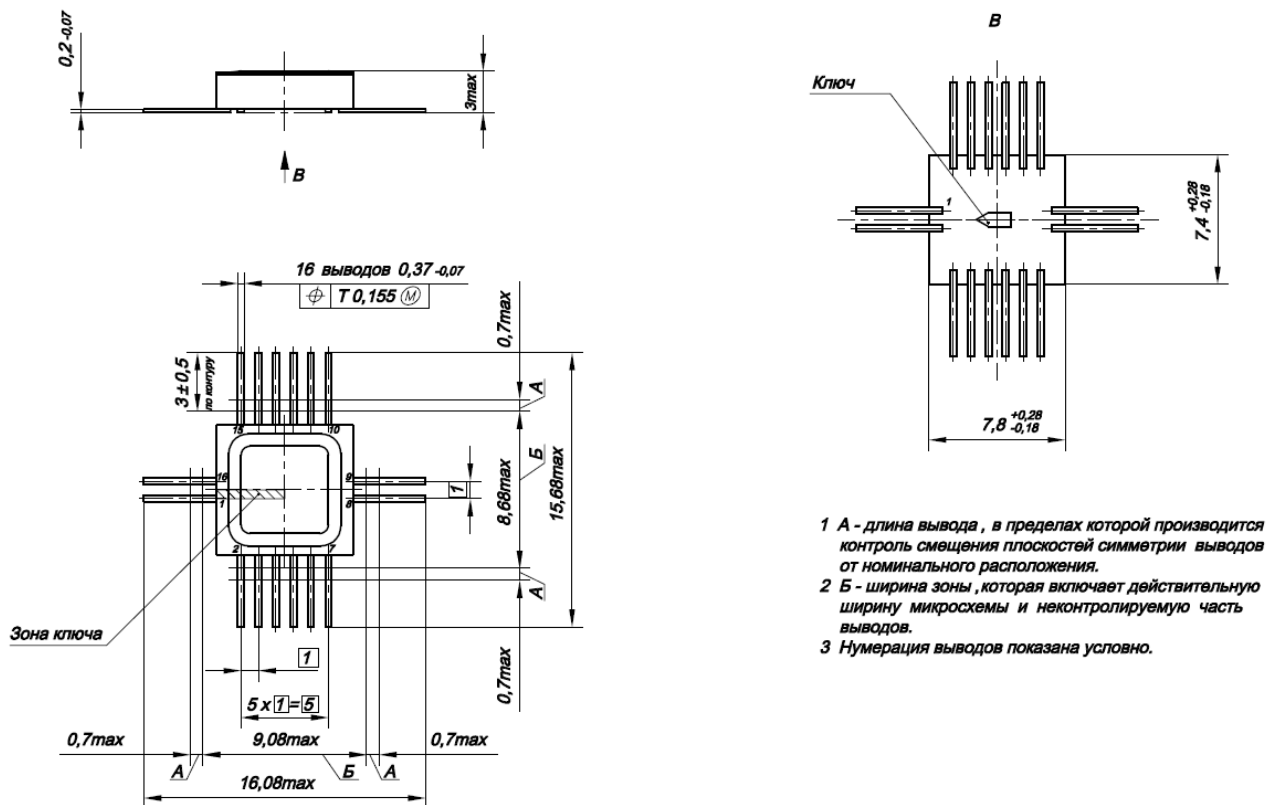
Габаритный чертеж корпуса Н04.16-1В
